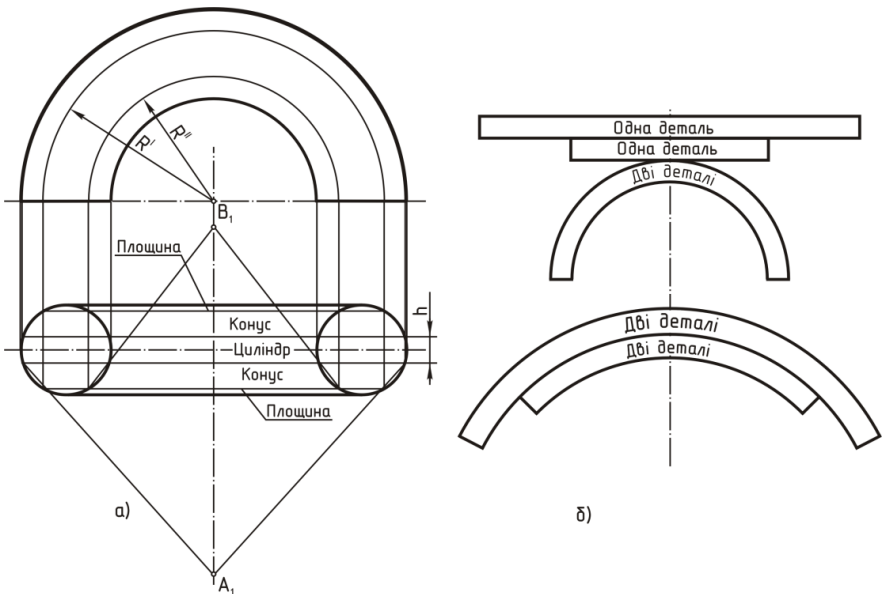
Розгортка поверхні тора: а) заміна поверхні тора розгорткованими поверхнями; б) наближена розгортка поверхні тора
